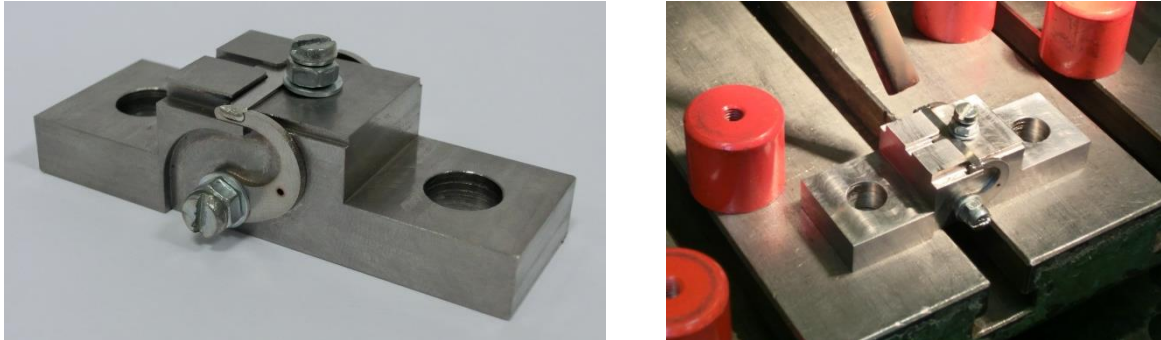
Klinken auf Schweißvorrichtung (links), Laserschweißen (rechts)
